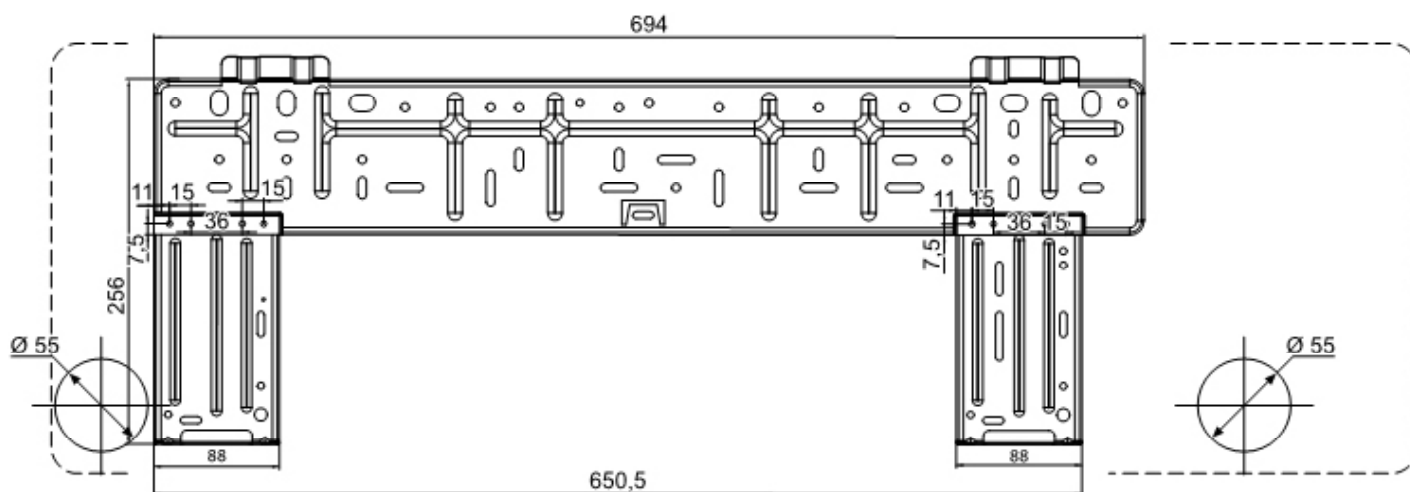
Placa de montaje para 3-050 WMNI.
